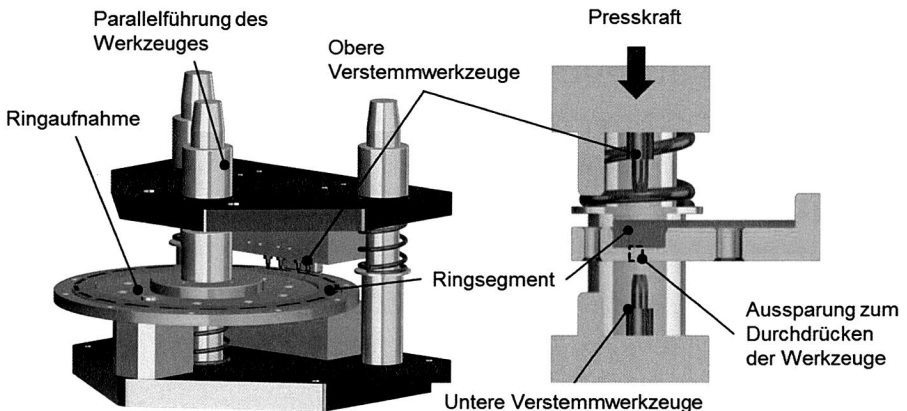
Links: Pressvorrichtung mit integrierten Verstemmwerkzeugen. Rechts: Schnittansicht.
